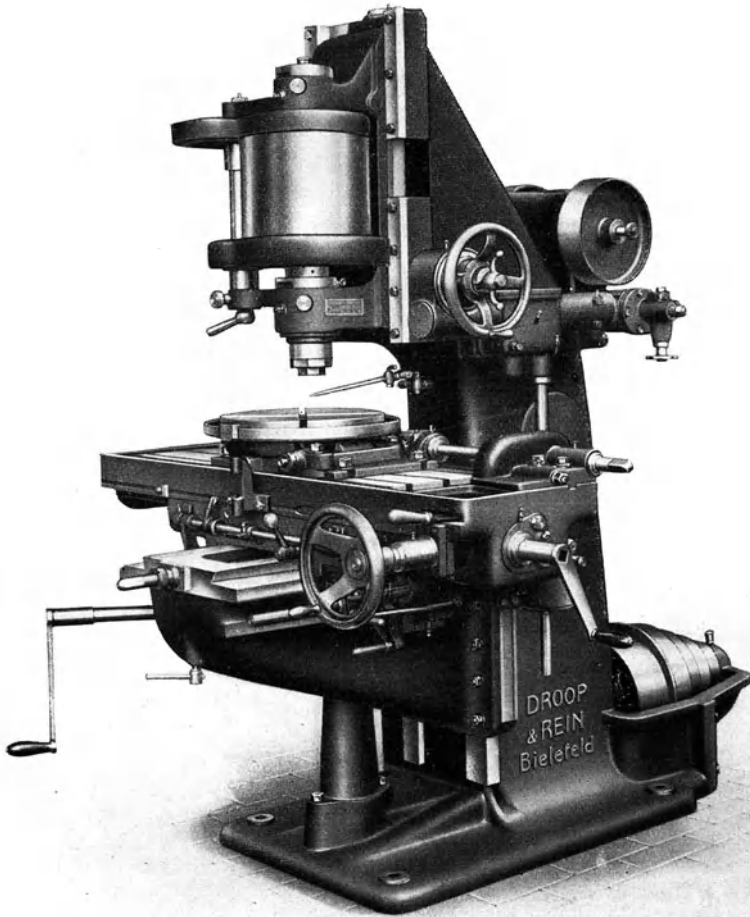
Die Senkrechtfräsmaschine von Droop & Rein.
